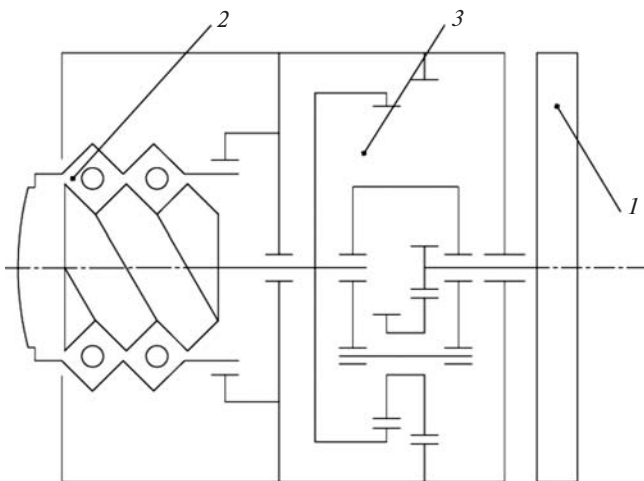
Схема модуля: 1 – ротор; 2 – выдвижной шток; 3 – редуктор
